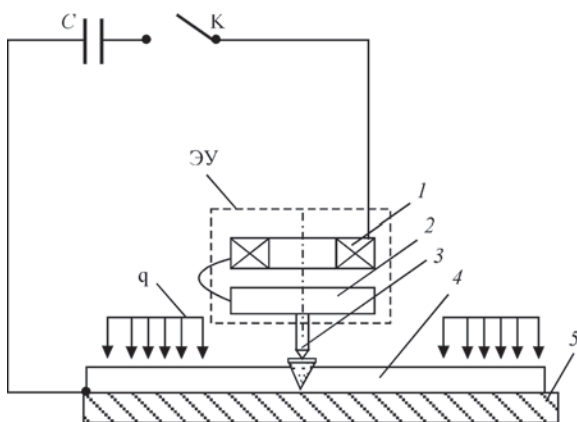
Схема ЭДО сварных соединений (C — емкостной накопитель энергии; К — силовой ключ; q — фиксирующая нагрузка); 1 — индуктор; 2 — диск; 3 — электрод; 4 — обрабатываемый металл; 5 — сборочная плита
